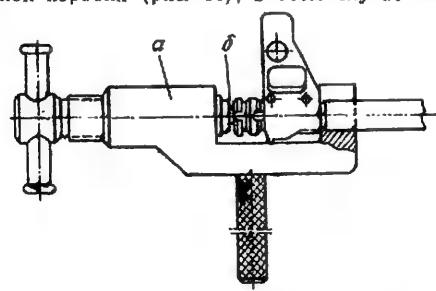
Схема установки струбцины: а — струбцина: б — стержень
